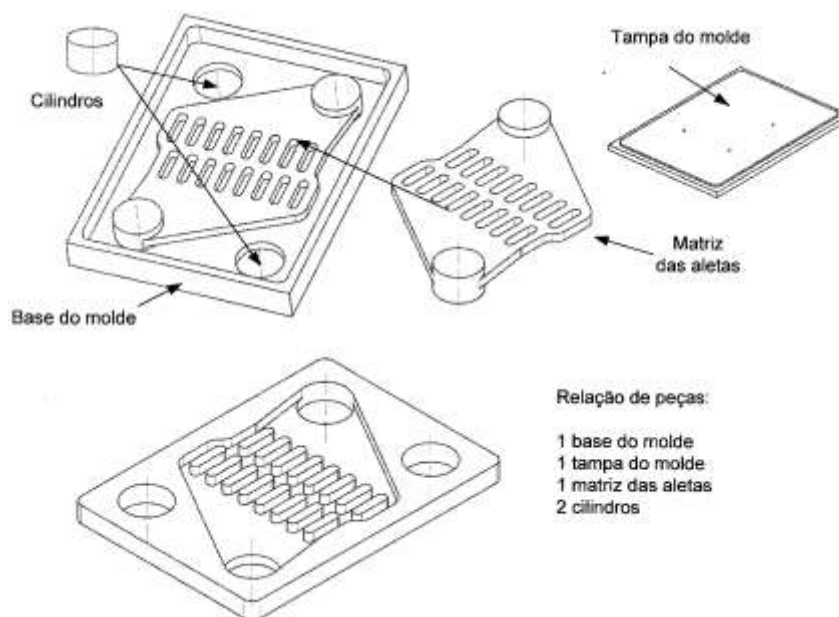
vista explodida do molde de alumínio usado para a confecção das primeiras peças.
